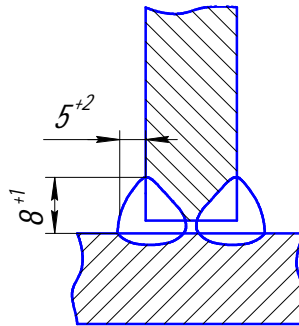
Схема таврового зварного з'єднання ТЗ
